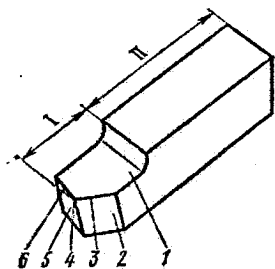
Типова конструкція токарного прохідного різця
